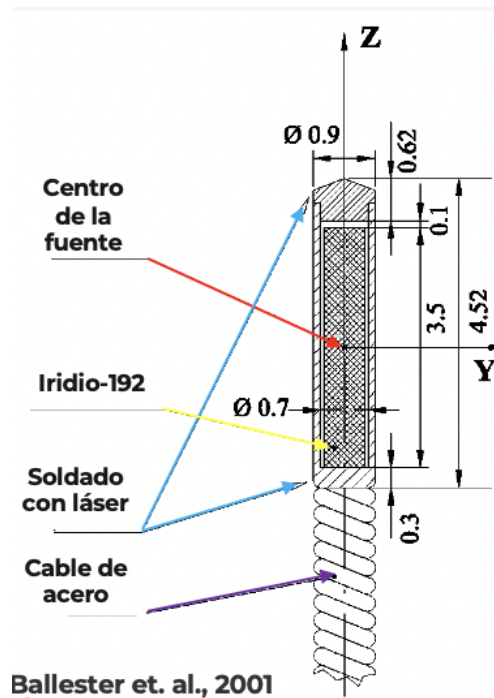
Diseño mecánico y geometría simulada de la fuente de Ir-192 para un sistema de carga remota GammaMed Plus. Las dimensiones mostradas se encuentran en mm y se considera a la fuente simétrica alrededor del eje z, imagen adaptada de Ballester, F. et.al., (2001). Monte-Carlo dosimetry of the HDR 12i and plus 192Ir sources, [34]
